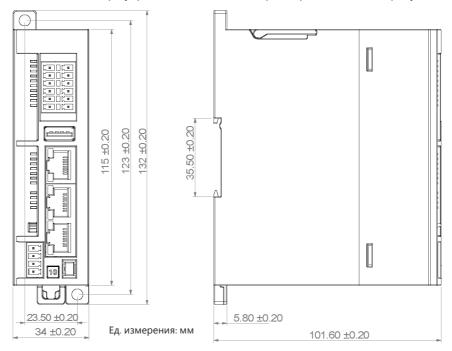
Монтажные размеры контроллера движений SM253CE10
